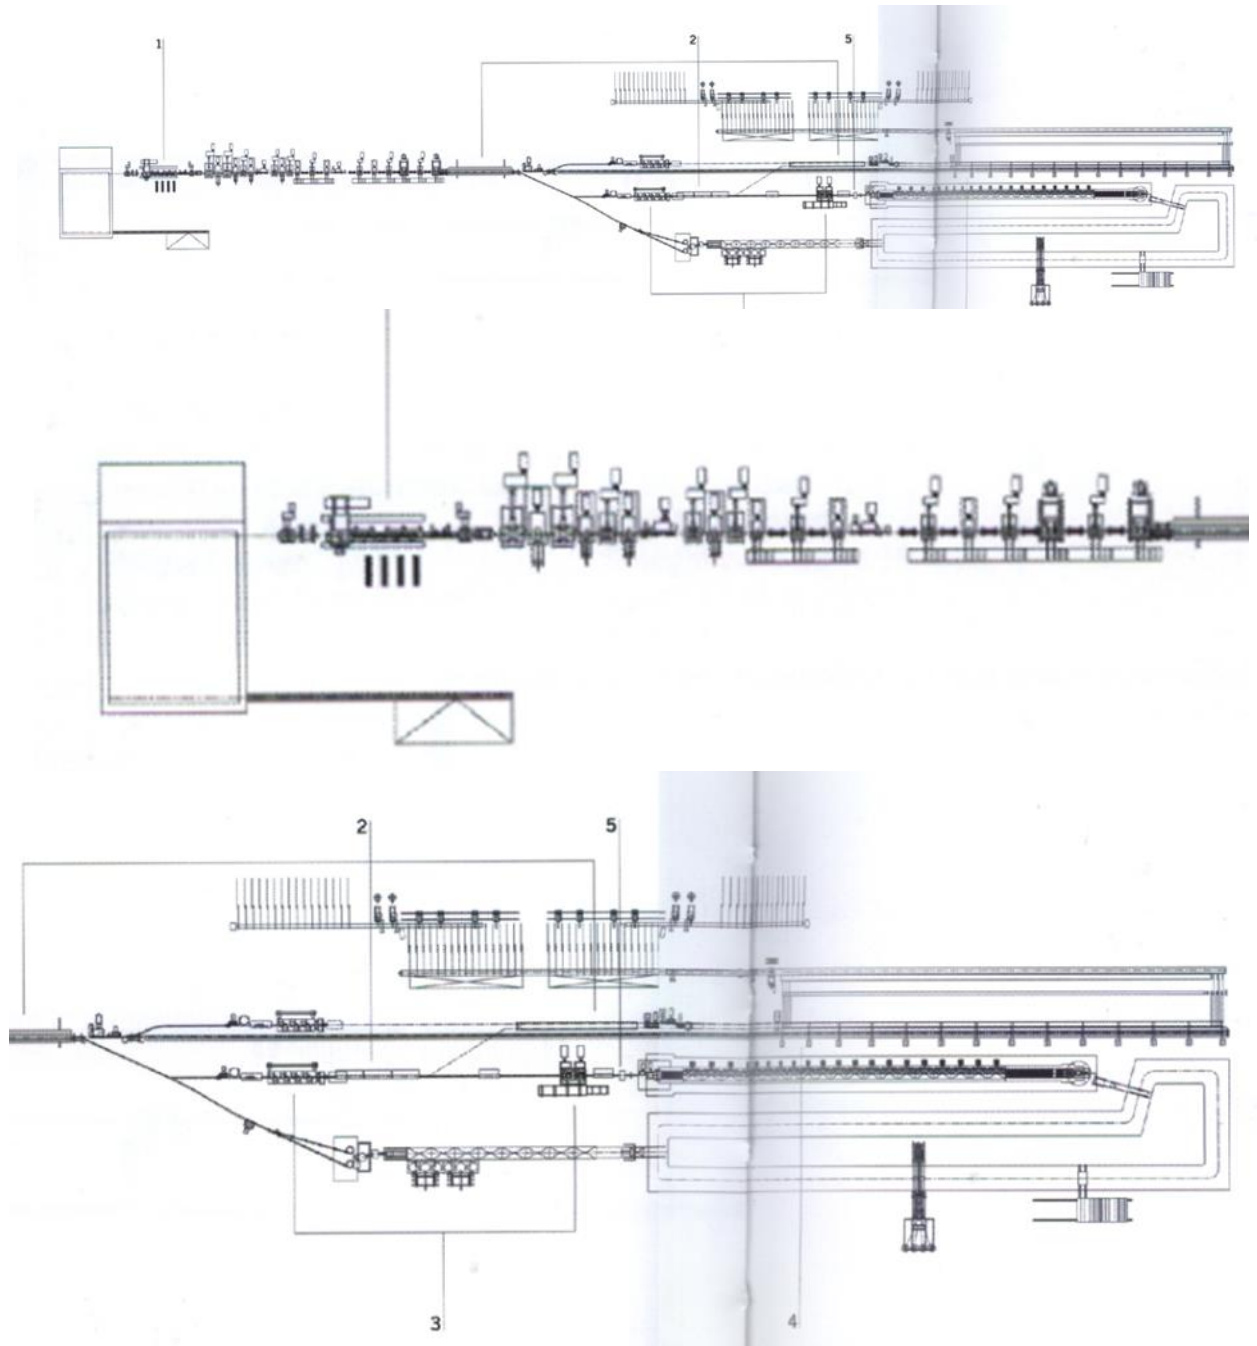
Схема розташування обладнання сучасного сорто-проволочного стану
